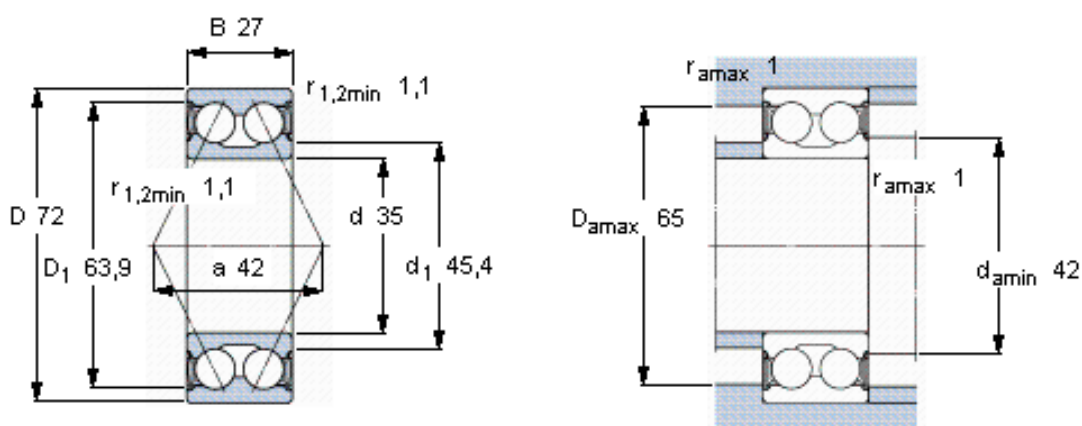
Rodamiento de bolas con contacto angular, de dos hileras²³.
